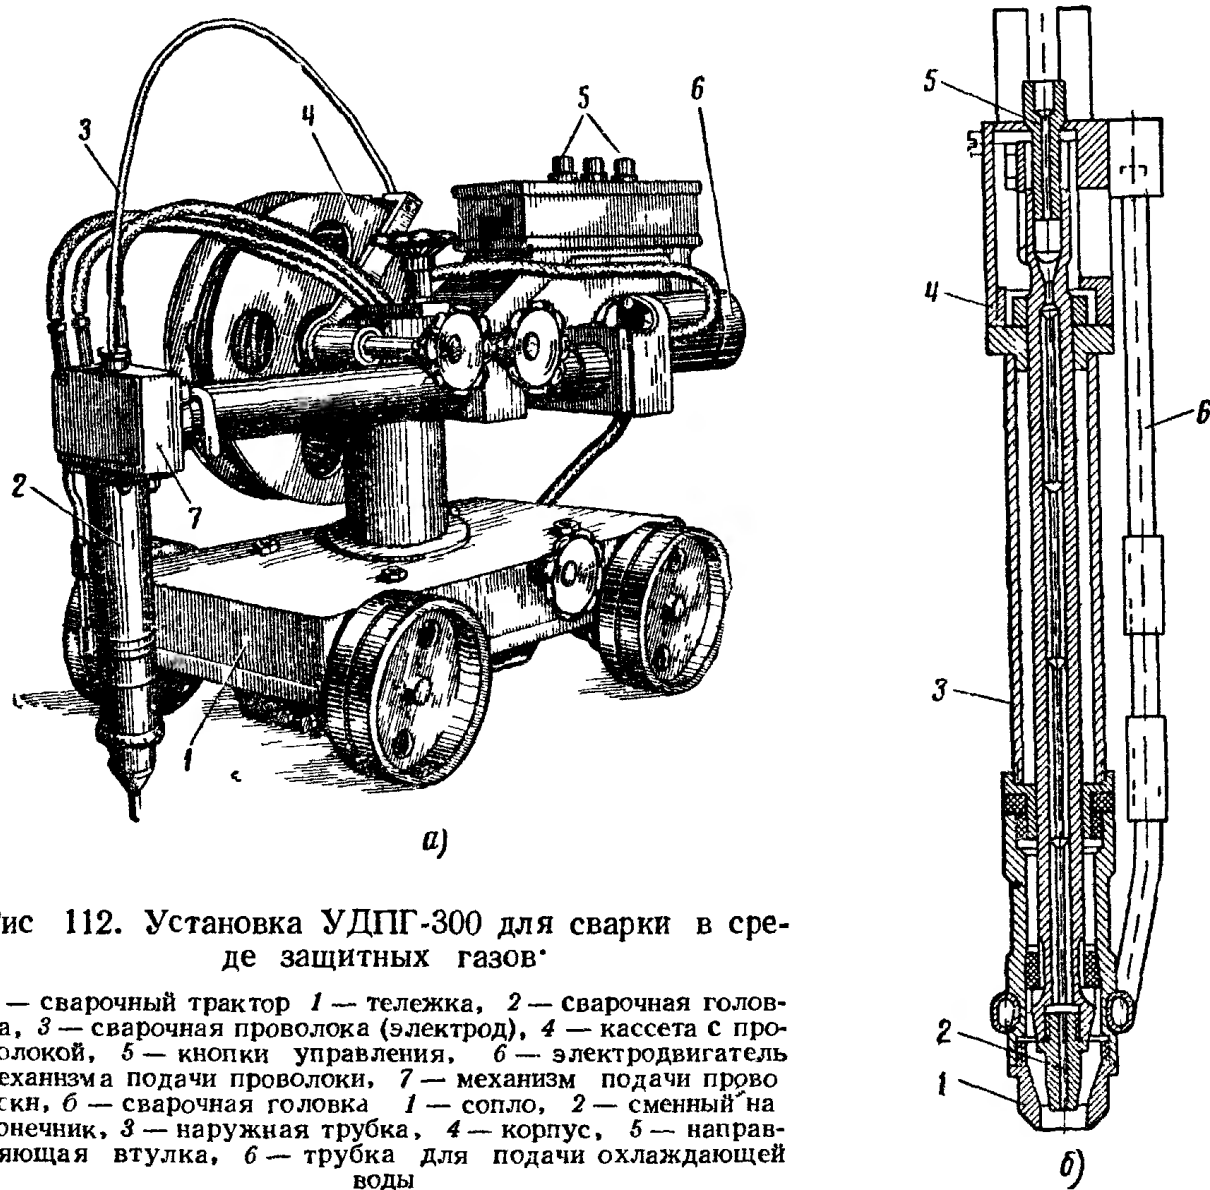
Установка УДПГ-300 для сварки в среде защитных газов.
